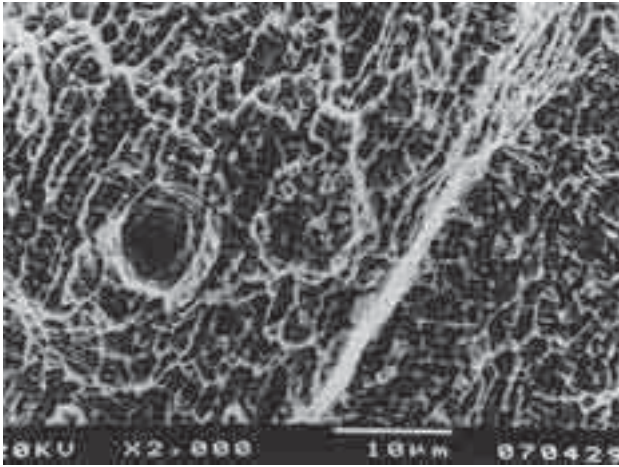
MEV da fratura dúctil por rasgamento do corpo-de-prova na condição soldado a laser; 2000X.
